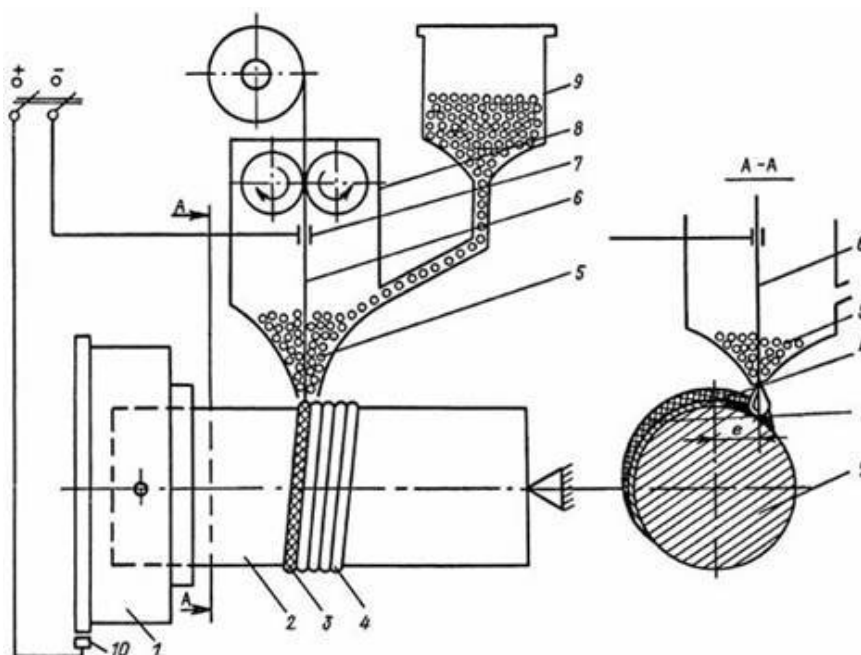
Схема установки для полуавтоматической электродуговой наплавки деталей
